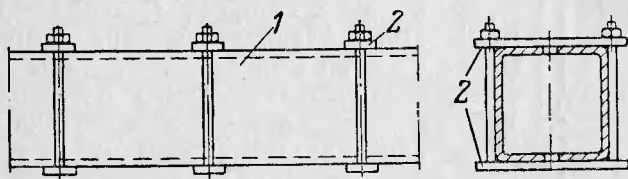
Шаблон для продольной сварки профильных шин.
